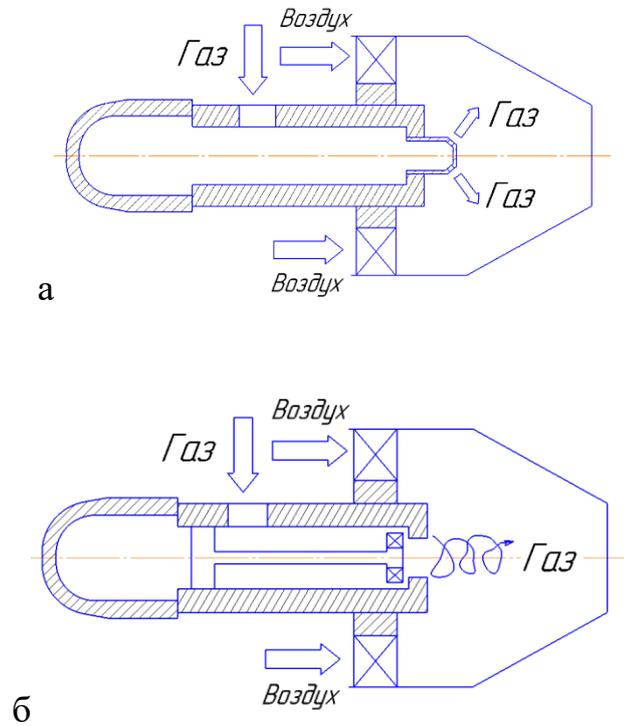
Схема форсунки а) струйная форсунка СГФ б) форсунка с подачей закрученной топливной струи ЦБГФ
